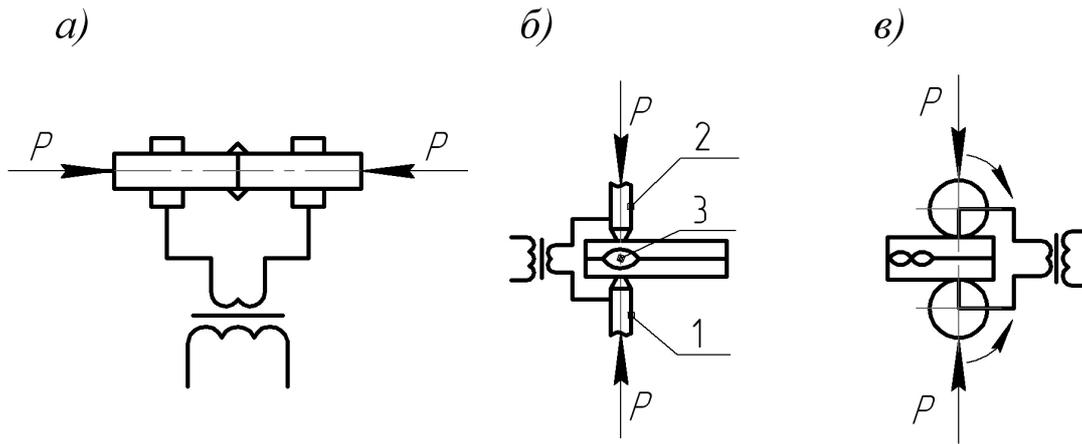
Схемы контактной сварки: *а* – стыковой; *б* – точечной; *в* – шовной; 1 и 2 – электроды; 3 – сварная точка
